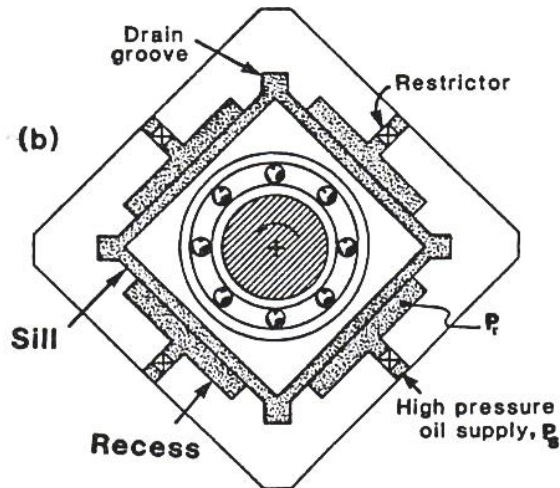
Paliers hybrides (Roulement - SFD patins plans), 1987 [2].
